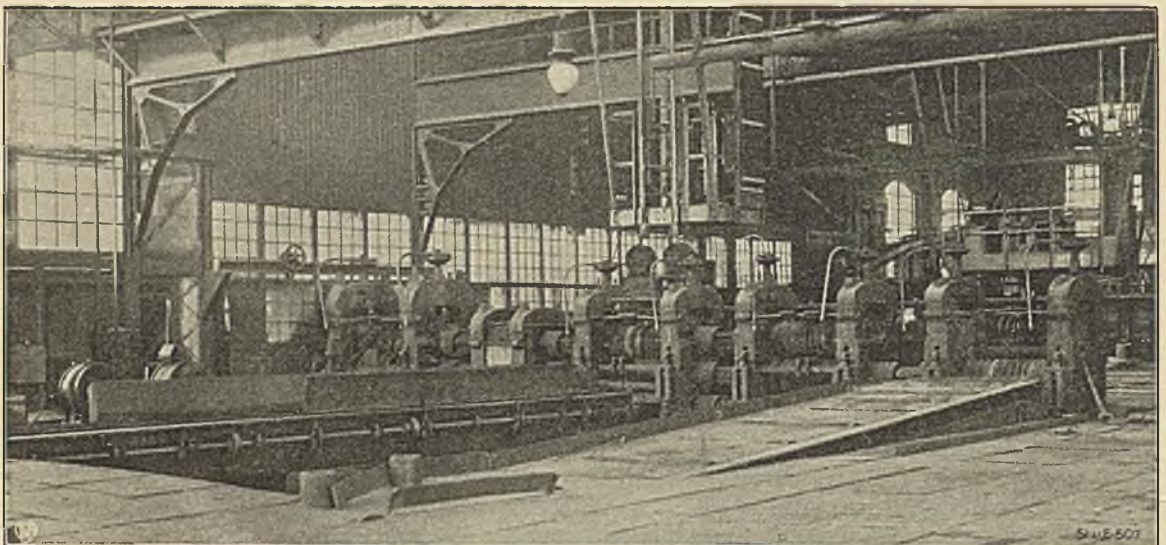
Platinenstrecke im Eisenwerk Althütten.
